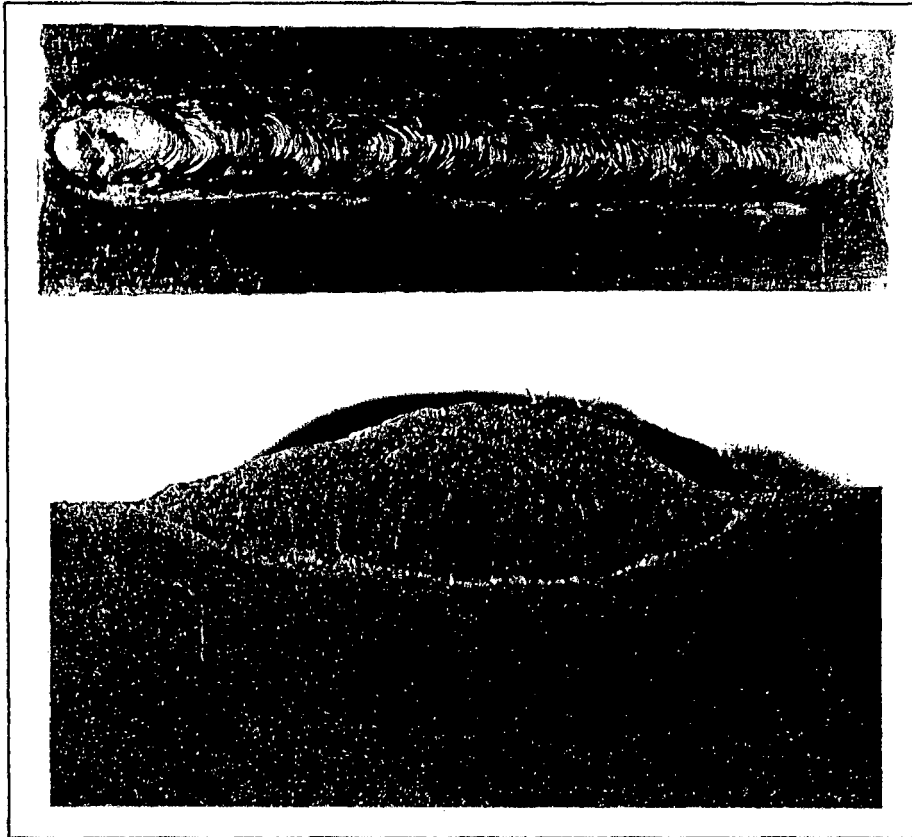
Aspecto do cordão de solda para o eletrodo H em CC+.
